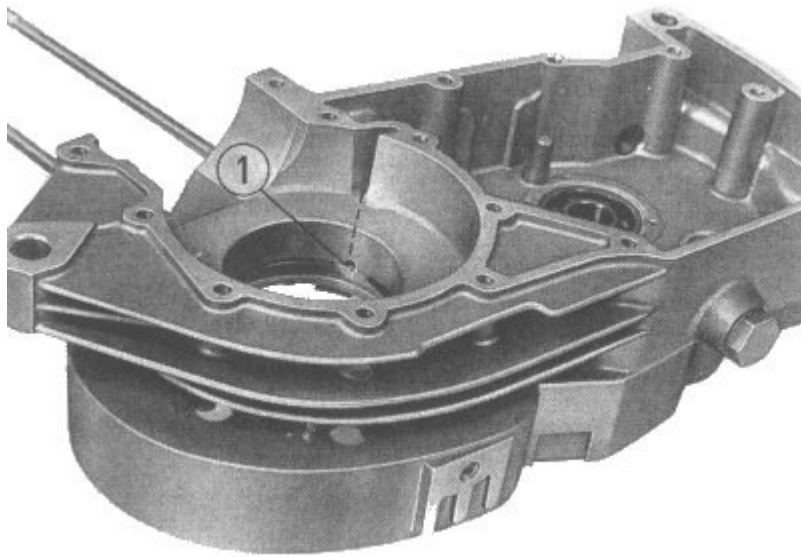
Kontrolle der Ölkanäle im Gehäuse
